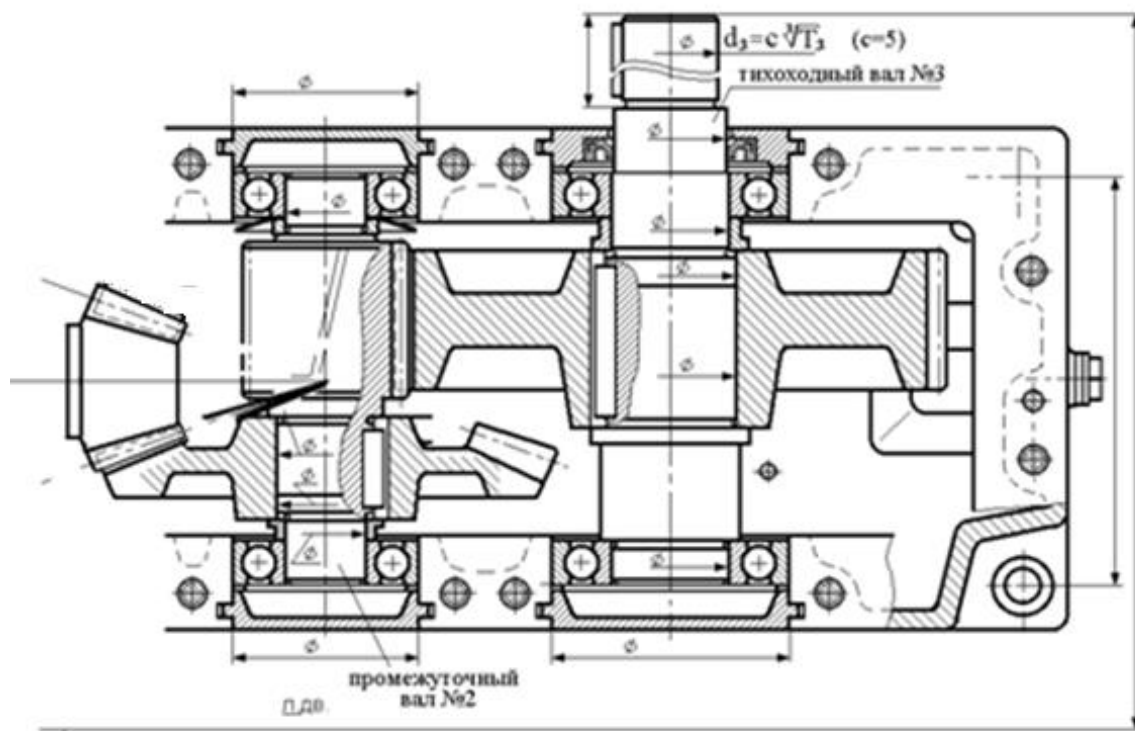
Промежуточный и выходной валы коническо-цилиндрического редуктора
